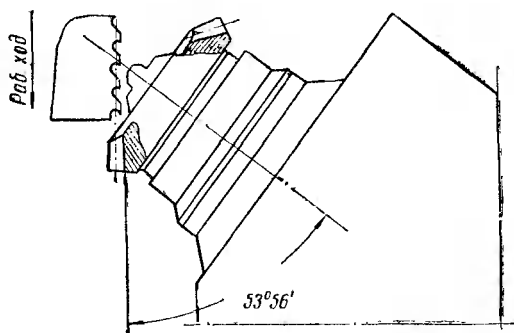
Схема предварительного протягивания зубьев конического зубчатого колеса
